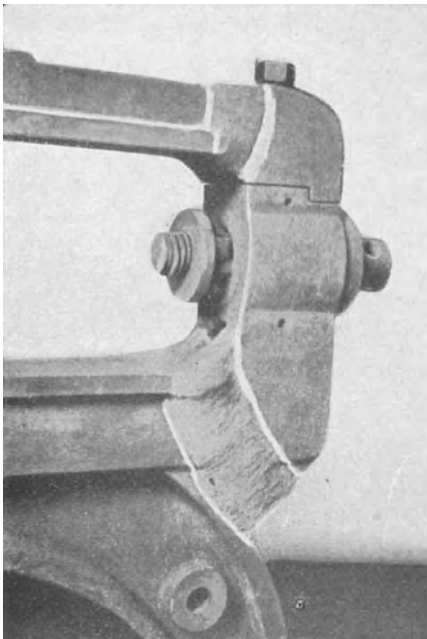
Schweißung am Ständer einer Gummiwalze.
